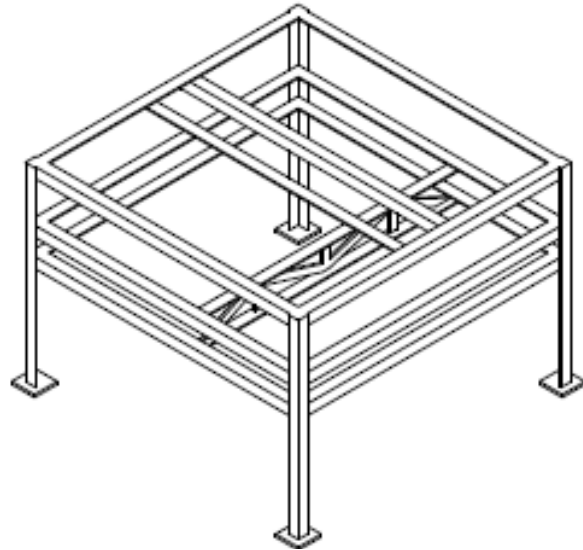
Estrutura Metálica da Centrífuga em CAD.
